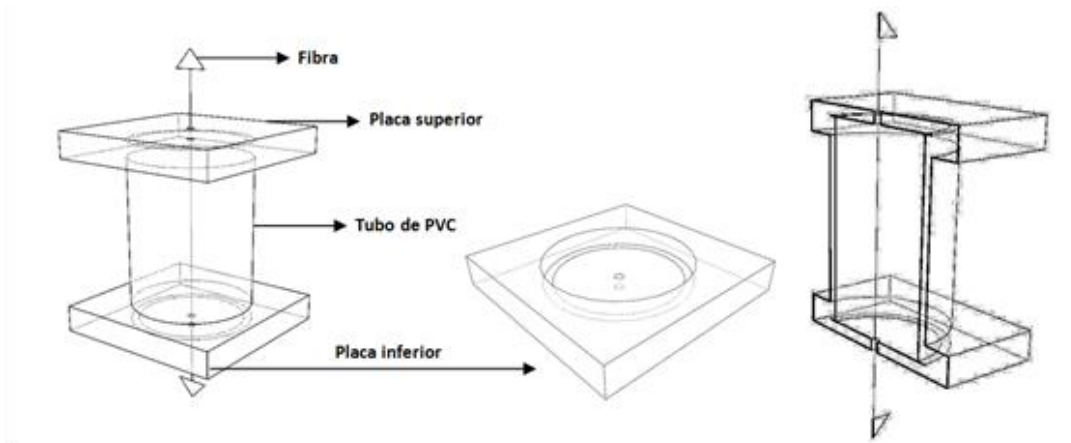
Molde utilizado no ensaio de arrancamento; Detalhe do rebaixamento para encaixe do molde de PVC; Corte do molde para provetes do ensaio de arrancamento
